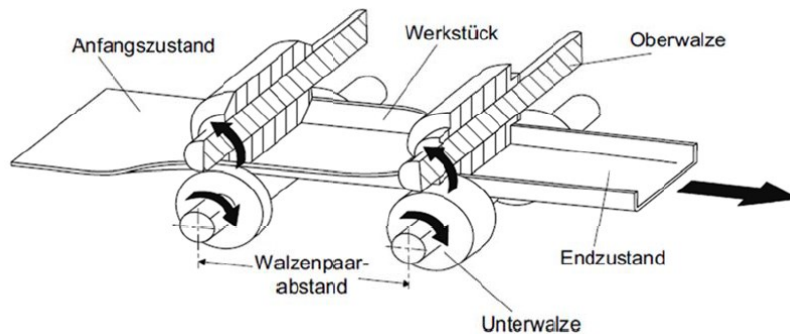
Herstellung eines U-Profils mittels Walzprofilieren [3]
